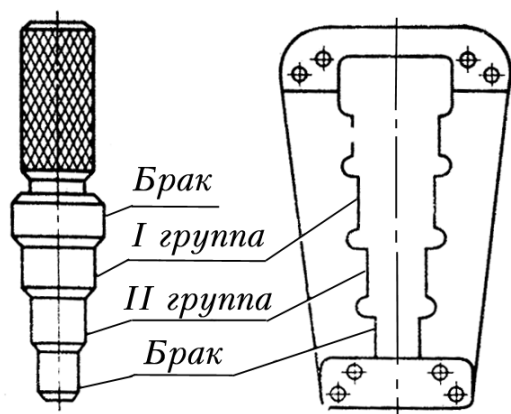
Калибры для рассортировки деталей на две группы.
